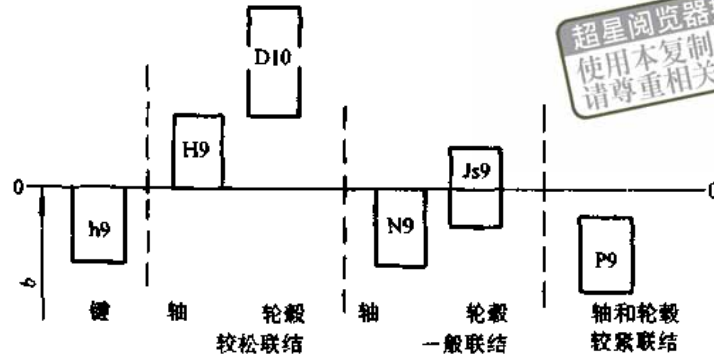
薄型平键配合尺寸 b 的公差带图
